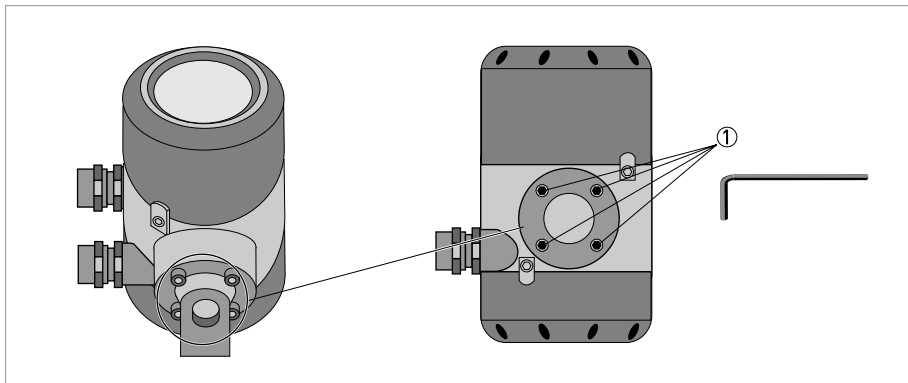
Innensechskantschrauben am Anschlussgehäuse
